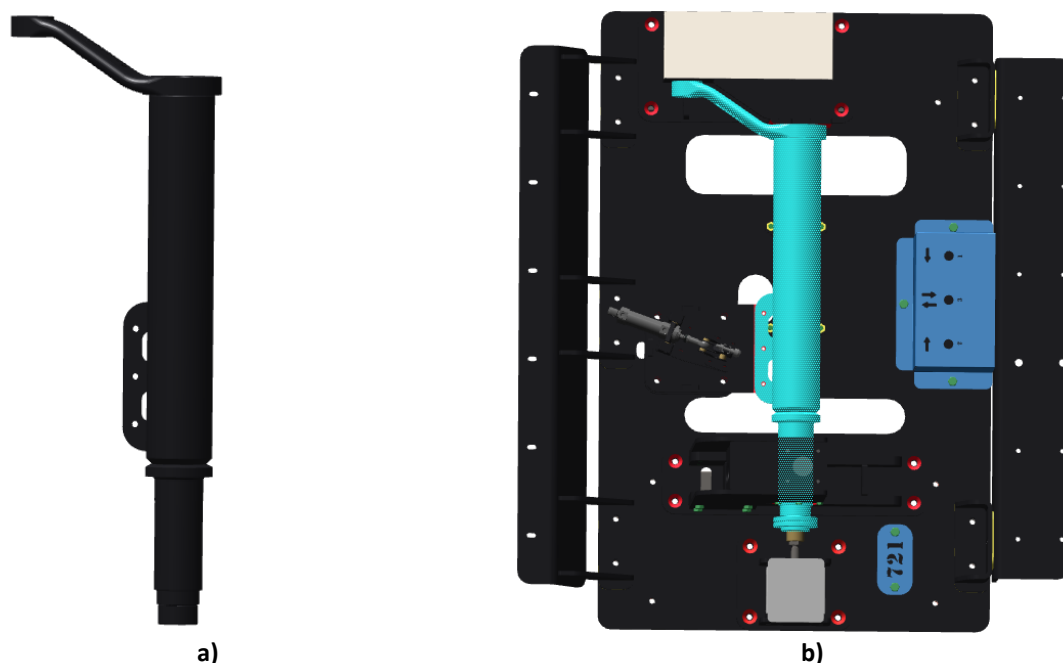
a) Desenho de peça 3D, b) Desenho do molde e respetiva peça em 3D
